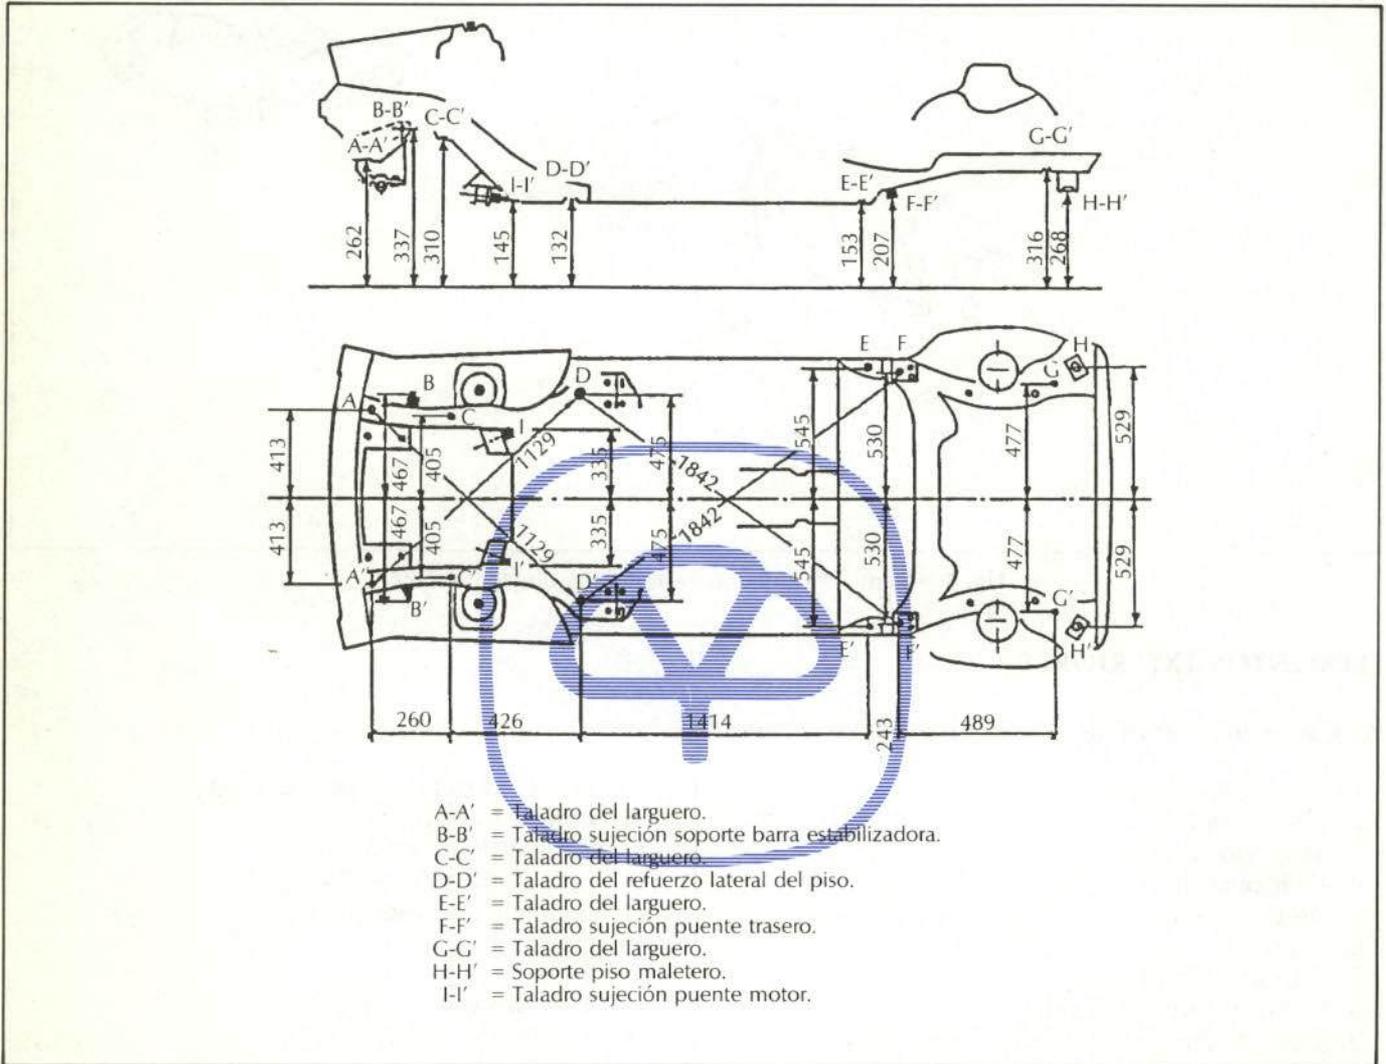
Dimensiones del vehículo en planta y alzado.
